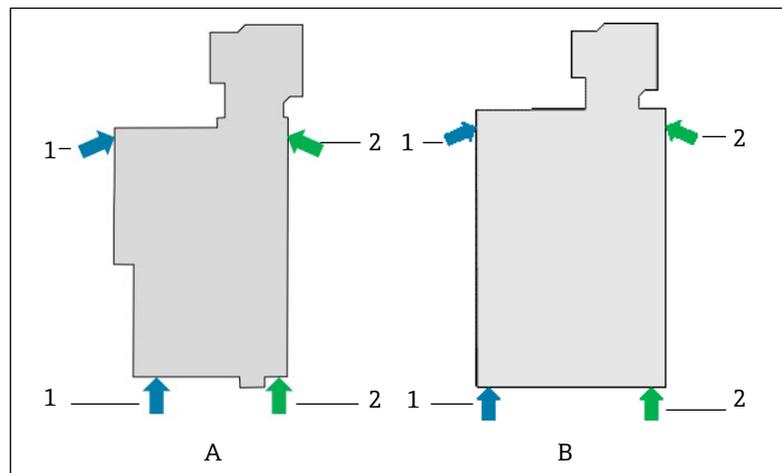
Positions de levage du J22 pour les installations sur panneau (A) et en boîtier (B)
